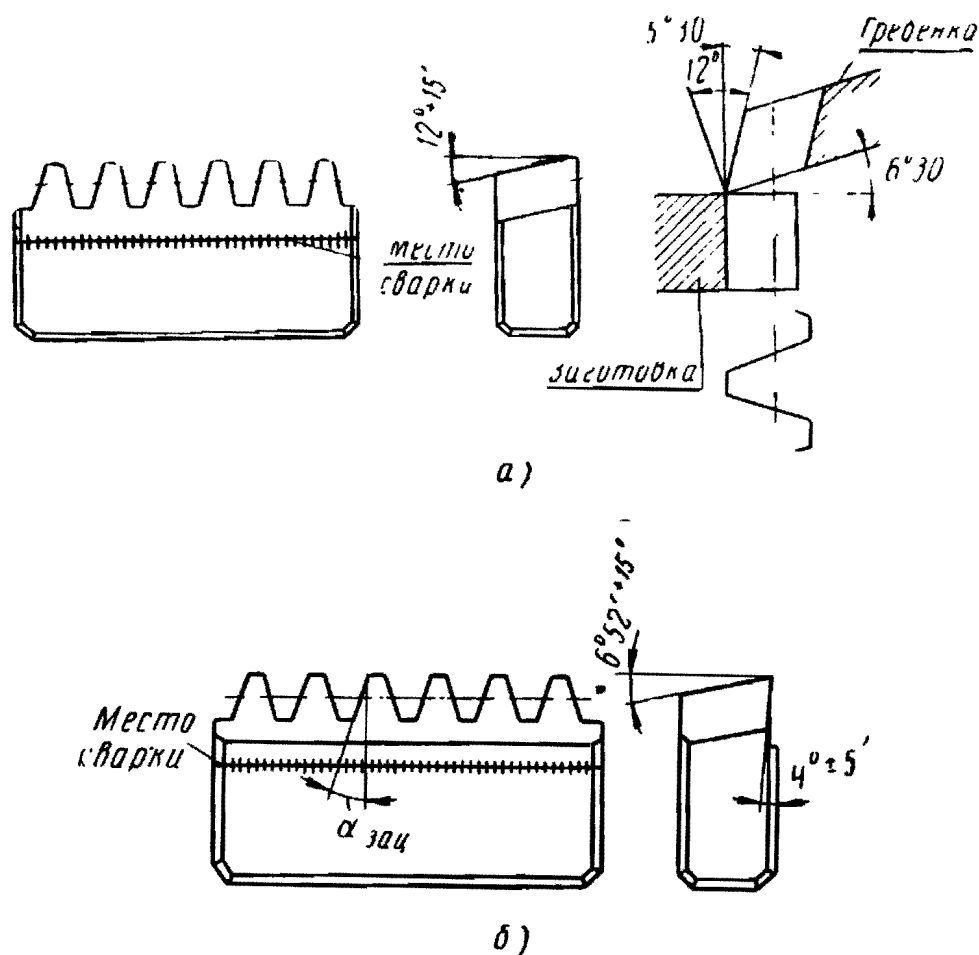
Прямозубые зуборезные гребенки для нарезания цилиндрических колес:
